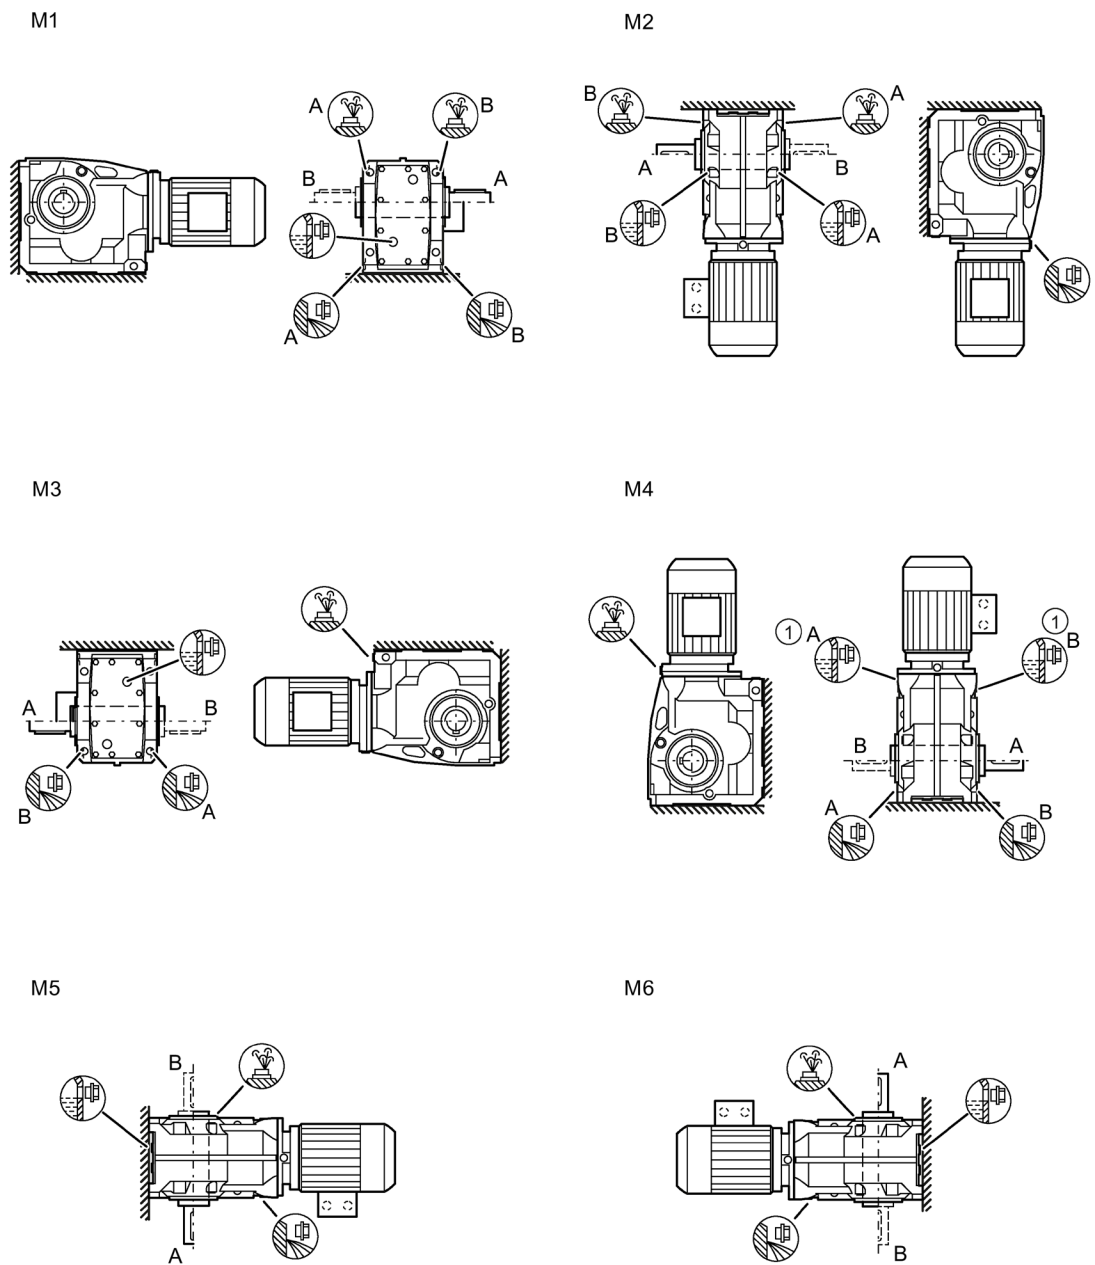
Einbautagen für Kegelradgetriebe K. Fußausführung Baugrößen 39 - 189
